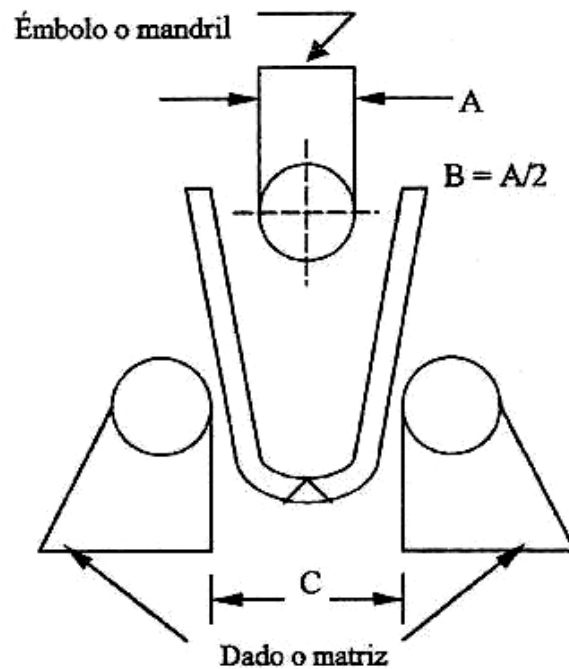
Dispositivo de prueba de doblado guiado y un espécimen de doblado de cara con la soldadura transversal.
